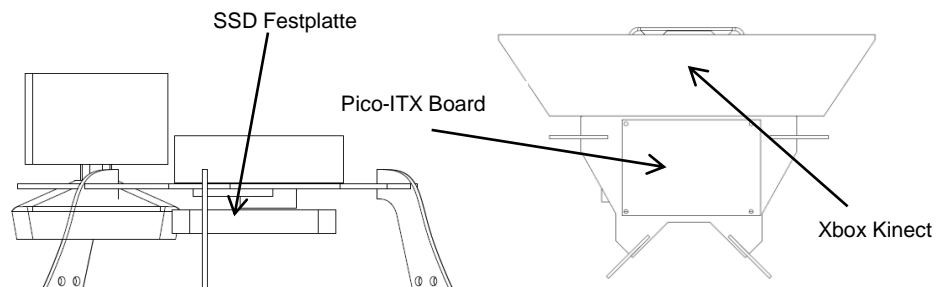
Seitenansicht (links) und Draufsicht (rechts) der Halterung für Xbox Kinect, Pico-ITX Board und SSD-Festplatte
